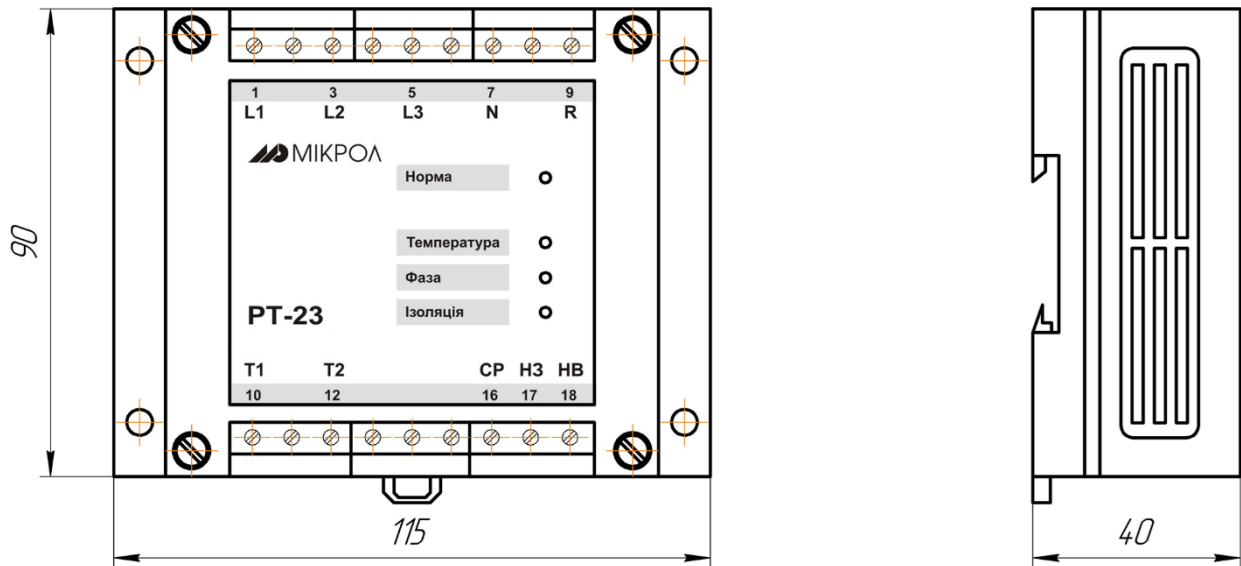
Зовнішній вигляд та габаритні розміри РТ-23
